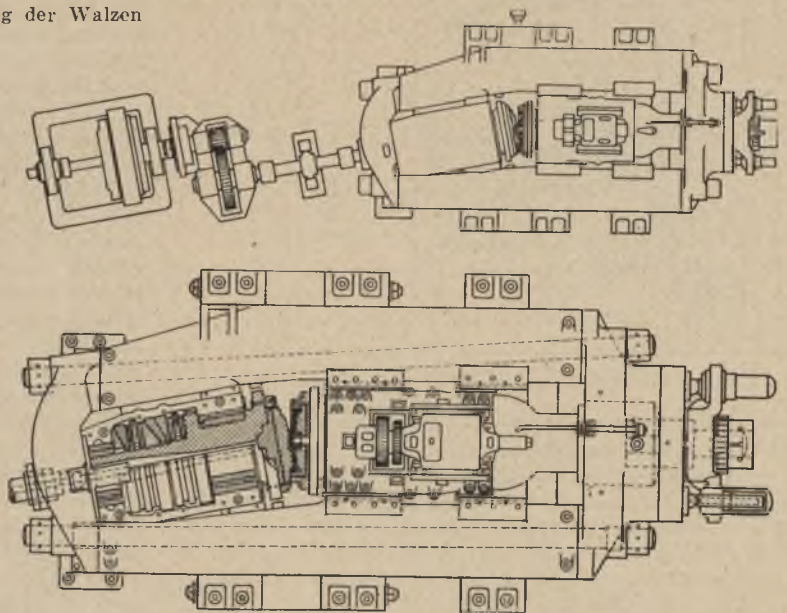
Radscheiben-Walzwerk nach E. Slick; Grundriß mit Antrieb.
